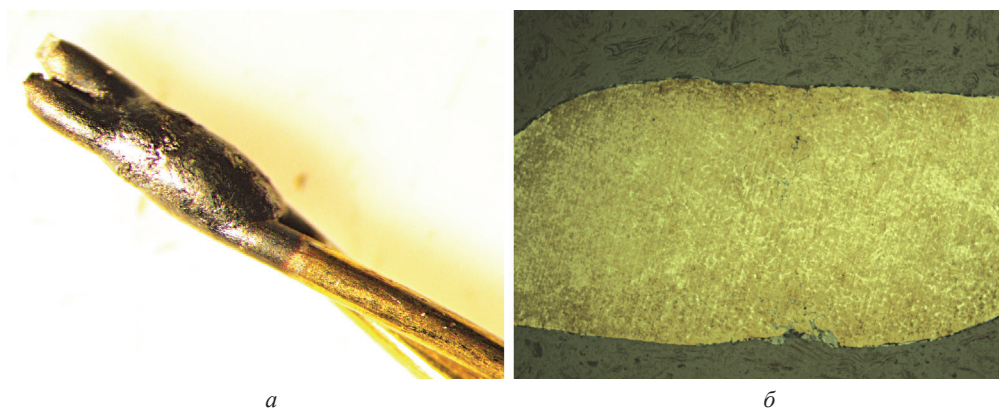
Сварка, выполненная согласно Регламенту (с полным отпуском) на металлокорде конструкции 2 \times 0,30 НТ: *a* – внешний вид разрушения после испытаний на разрыв. $\times 10$; *б* – мартенсит отпуска в микроструктуре сварного шва. $\times 200$
